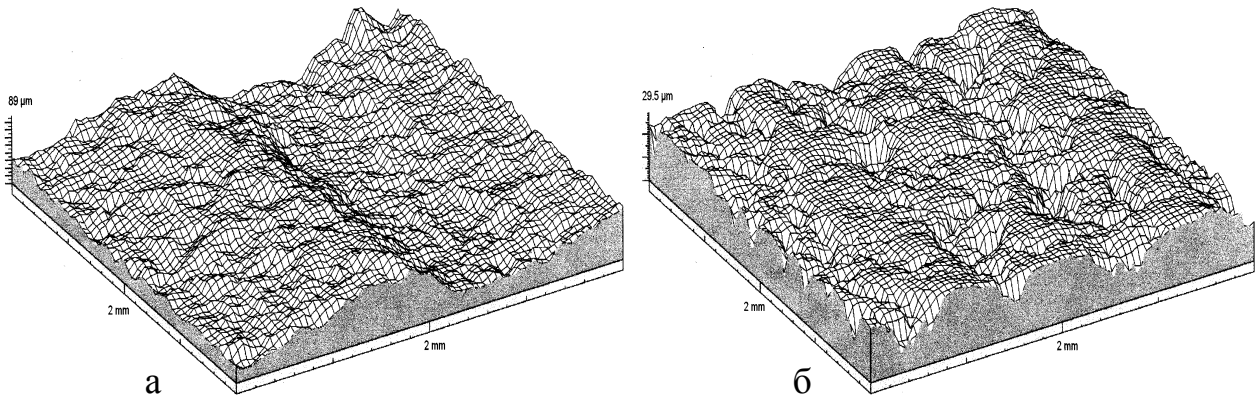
Аксонометричні зображення поверхні деталей: а – після фрезерування; б – після вібраційної обробки на вібраційних машинах з торовидною робочою камерою
